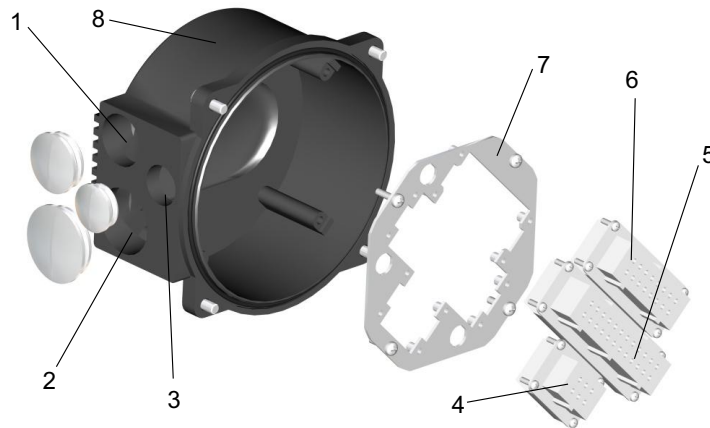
1... metrische Verschraubung (sind bei Auslieferung mit Blindschrauben verschlossen) M32x1,5, 2... M40x1,5, 3... M25x1,5, 4... Steckereinsatz (für Spannungsversorgung), 5... Steckereinsatz (für Steuerleitungen), 6... Stecker für Optionen, 7... Steckerblech, 8... Anschlussgehäuse
